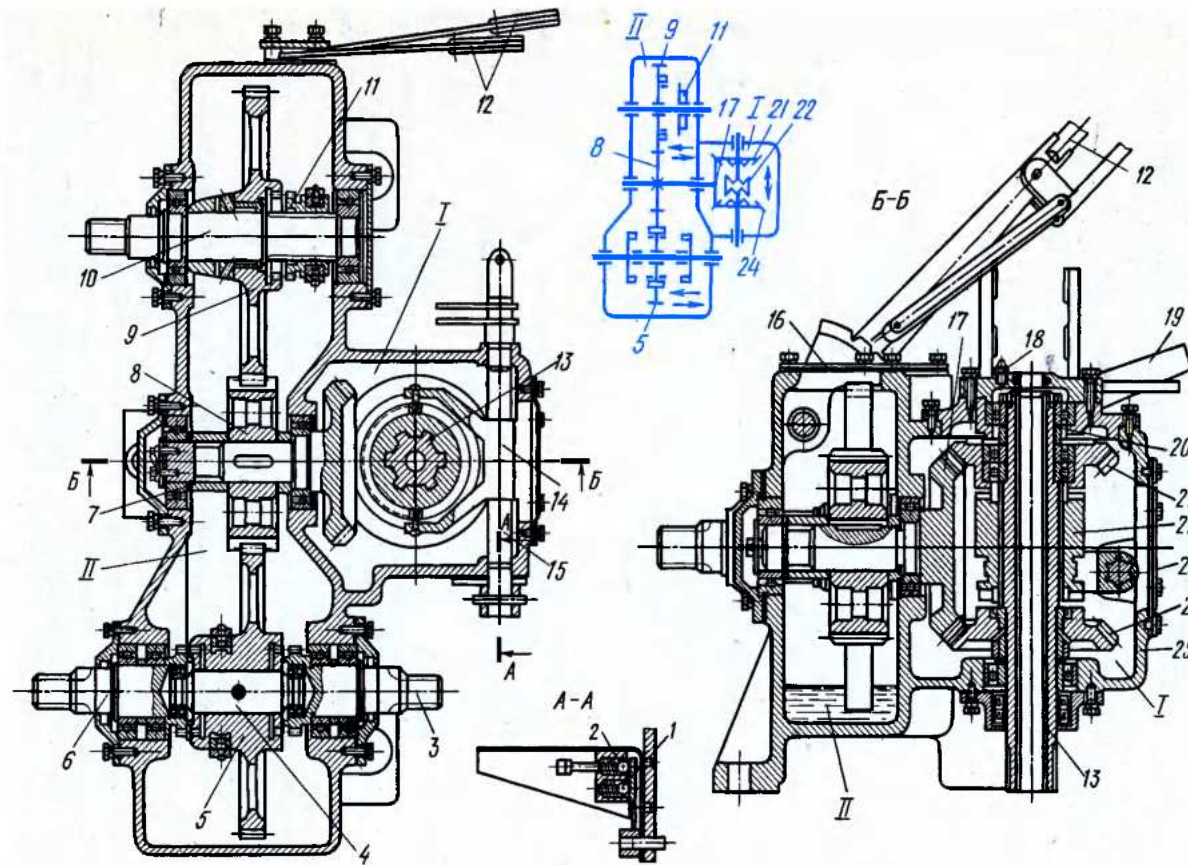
Реверсивно (I)-распределительный (II) механизм крана КС-2561Д;
